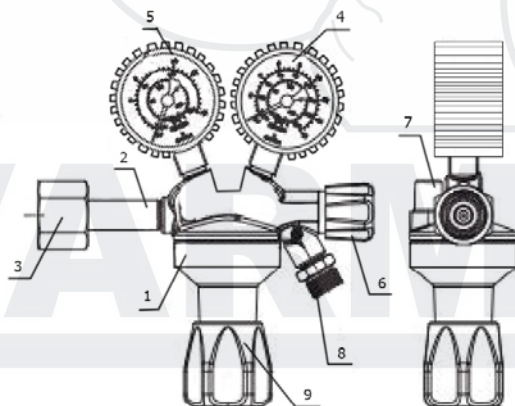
Схема редуктора баллонного газового TECH CONTROL OX (кислород), CD (углекислота), UNI (аргон, азот, гелий).
